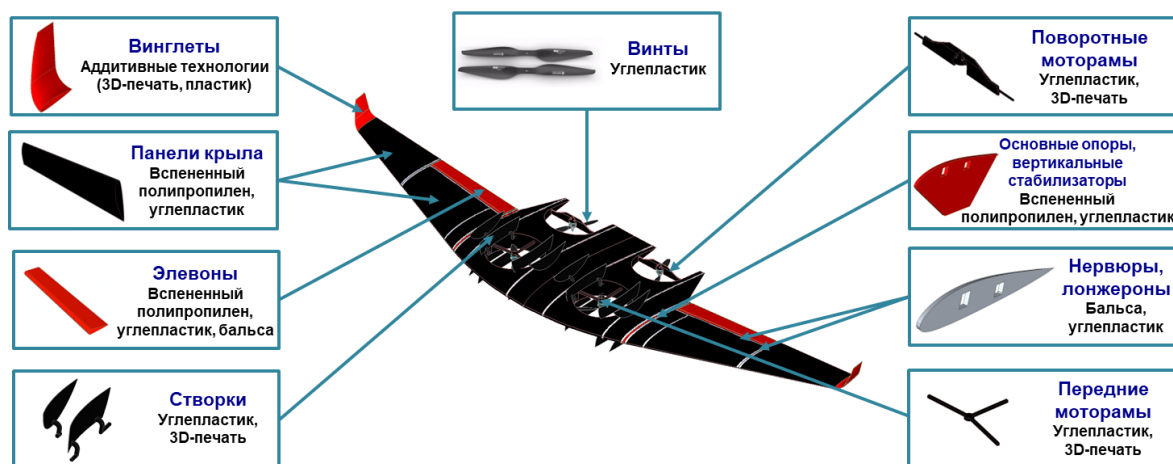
Компоновка конструкции БПЛА «Снегирь-1»
